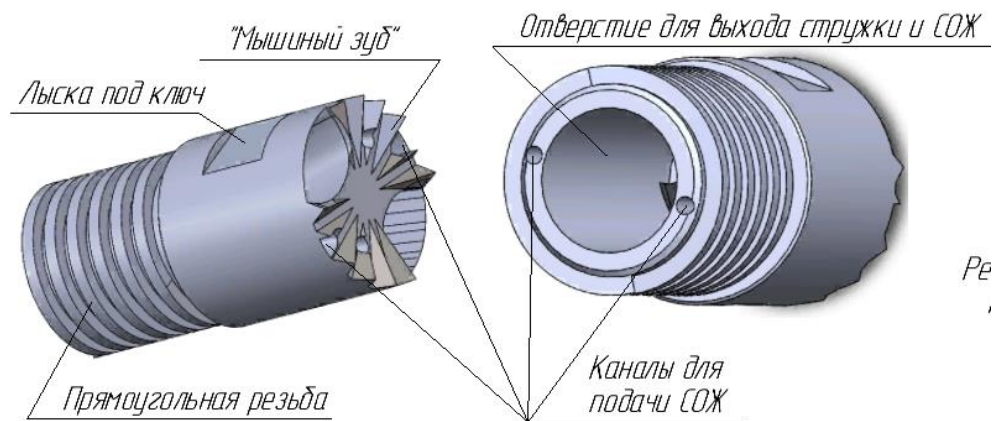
Вид корпуса нового сверла с базовыми поверхностями для установки режущей головки и удлинителя
